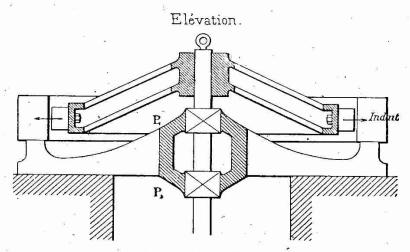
Alternateur vertical « à parapluie » Brown-Boveri. Coupe par un plan axial.
